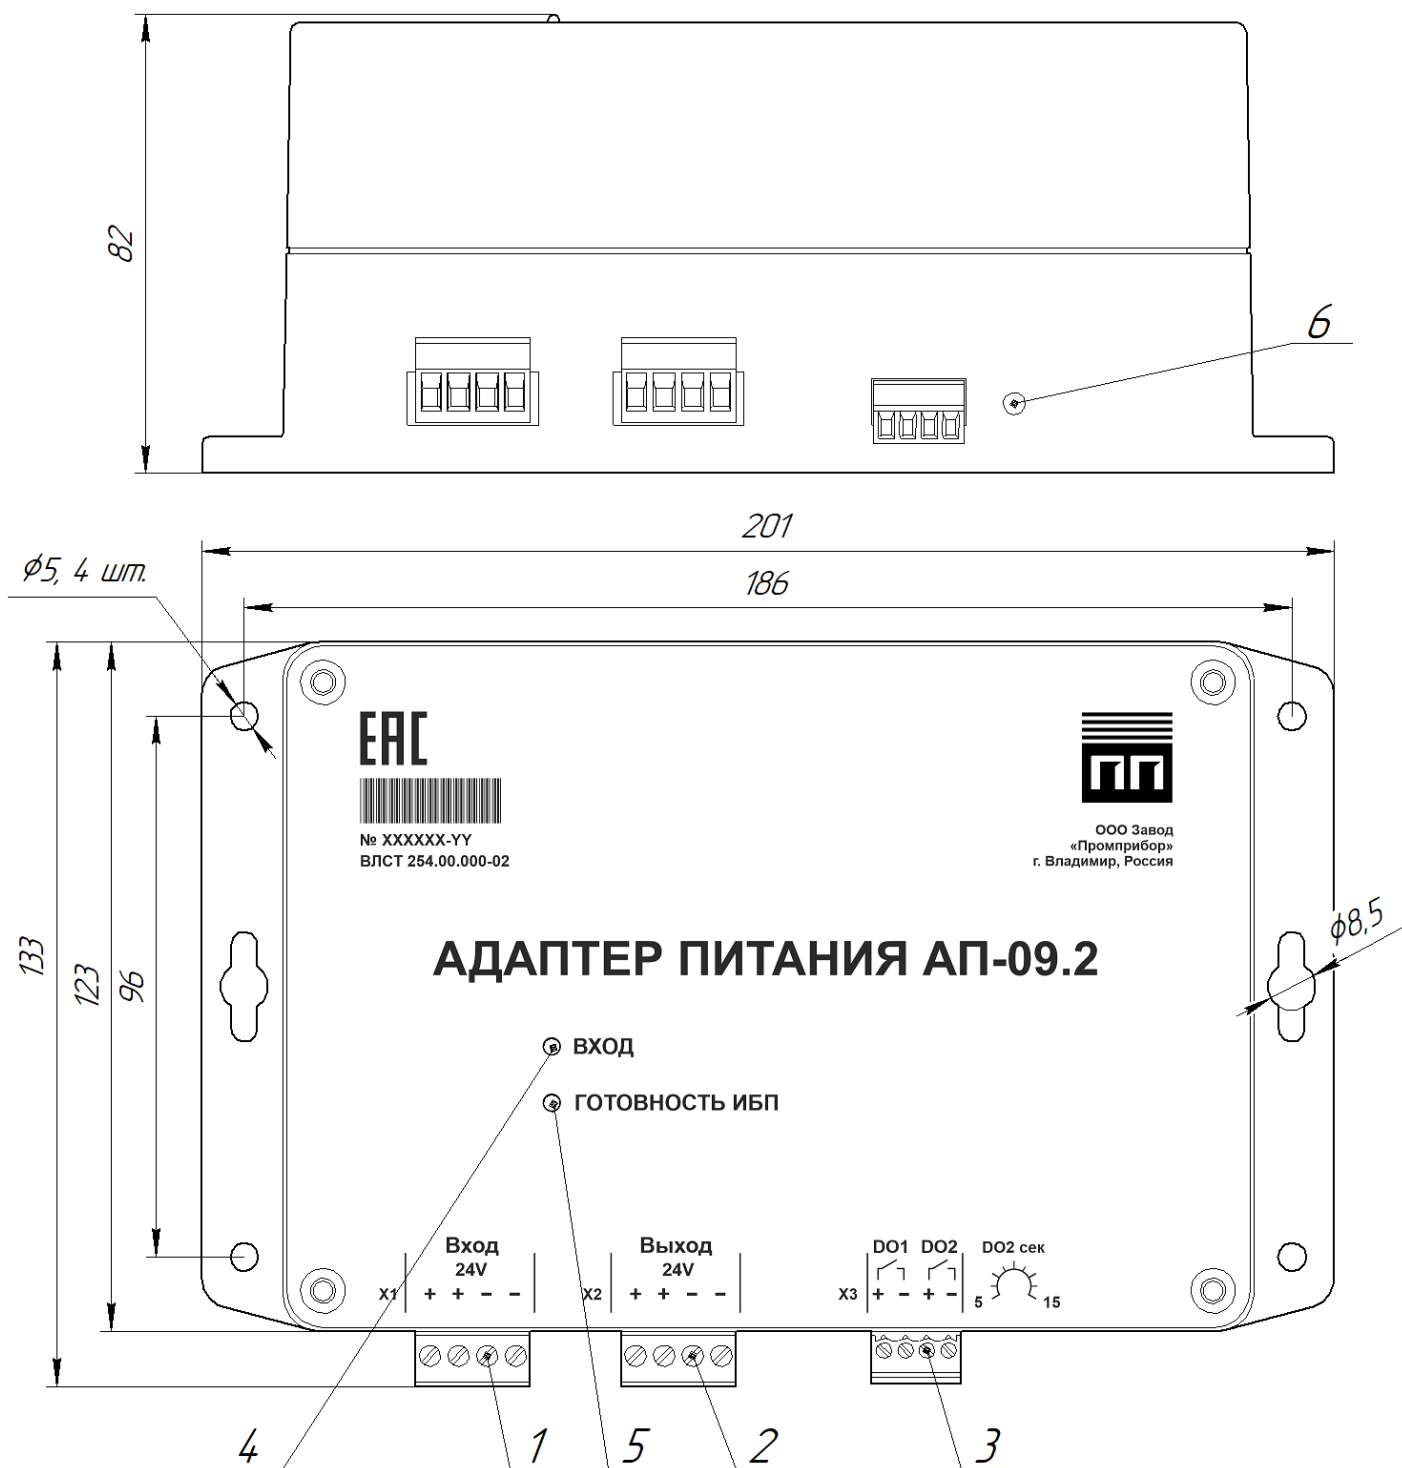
Внешний вид и размеры адаптера АП-09.2
